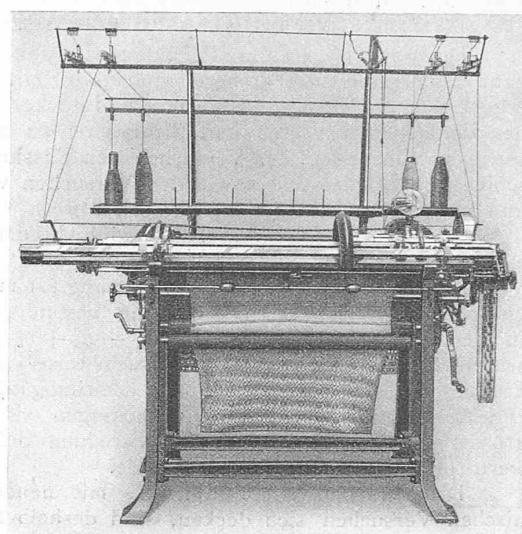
Halbautomat. Jacquard-Strickmaschine mit Motorantrieb.
